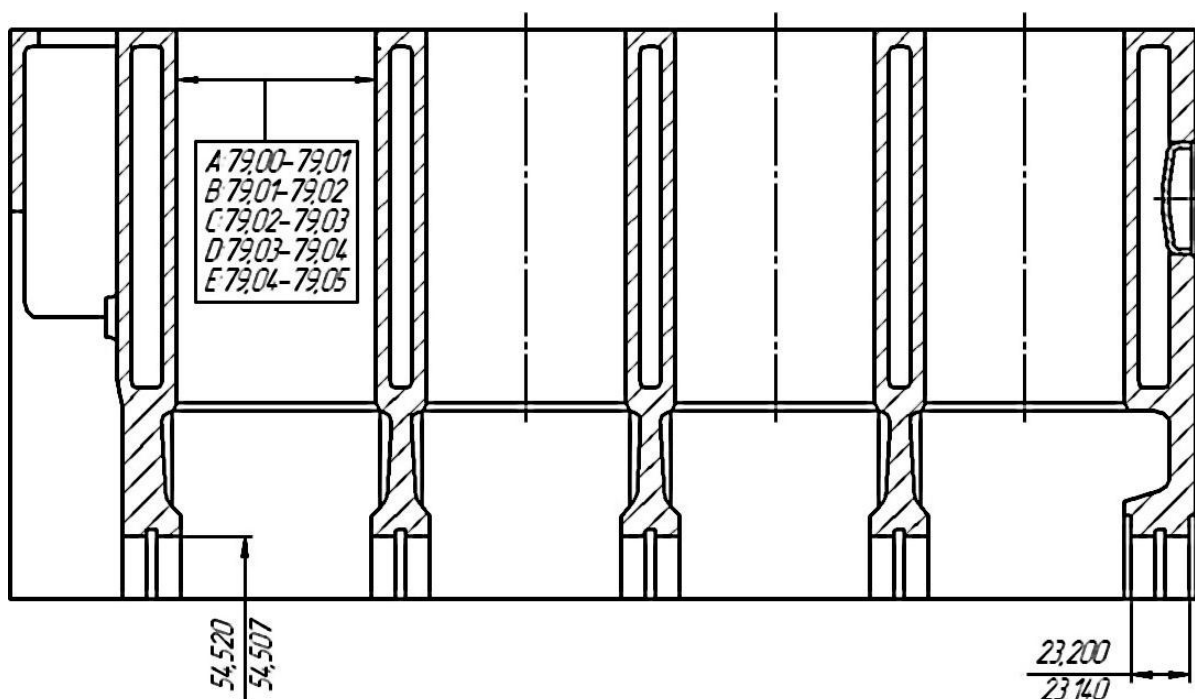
Контролируемые размеры блока цилиндров двигателя
